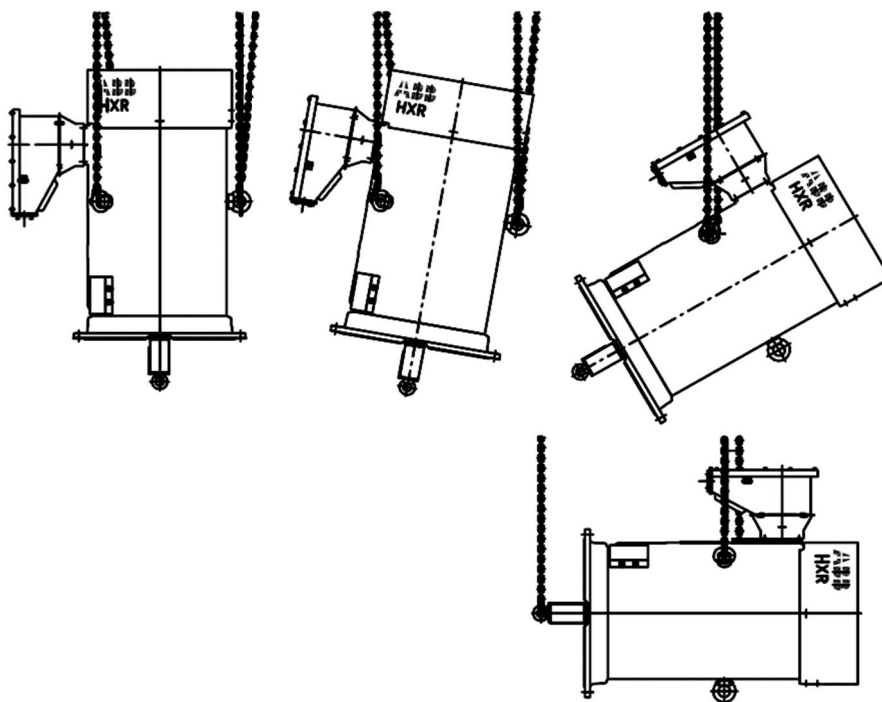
Máquina com olhais de elevação giratórios: elevação e giro
